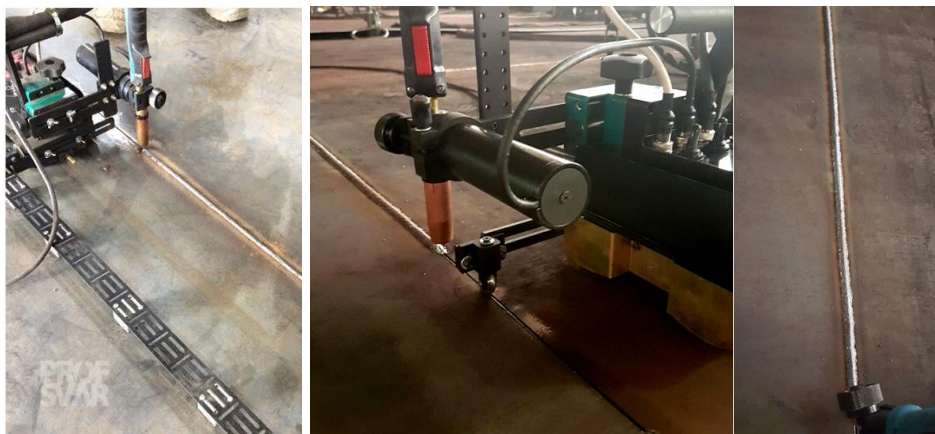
Каретка сварочная на монтаже резервуара
